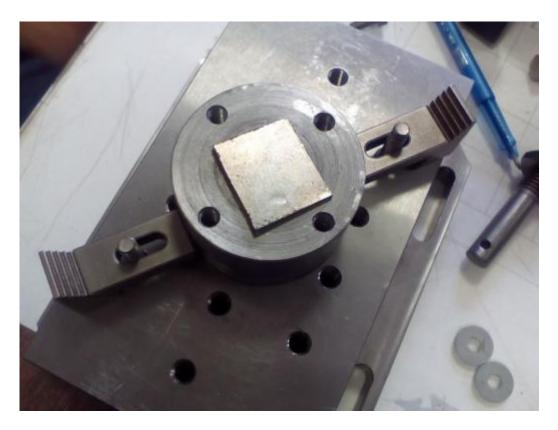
Заготовка и фиксирующее устройство до закрепления на динамометре
